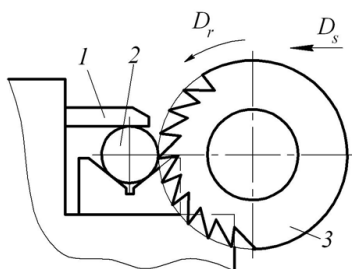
Схема отрезки заготовок на круглопильном станке
